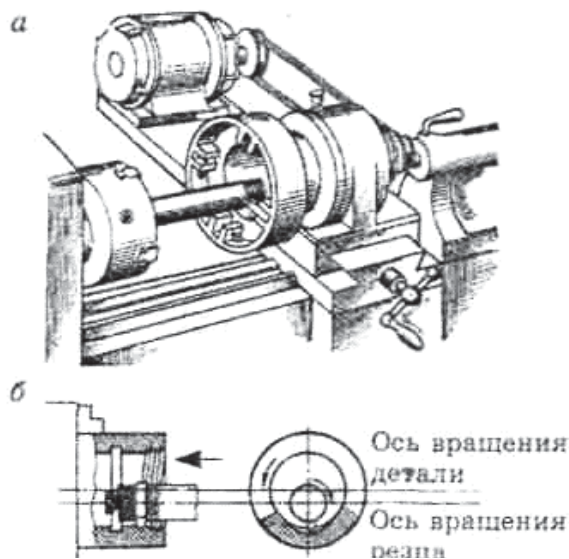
Нарезание резьбы вращающимися резцами: а – головка для резцов (в положении, показанном на рисунке, установлен только один резец); б – схема нарезания внутренней резьбы
